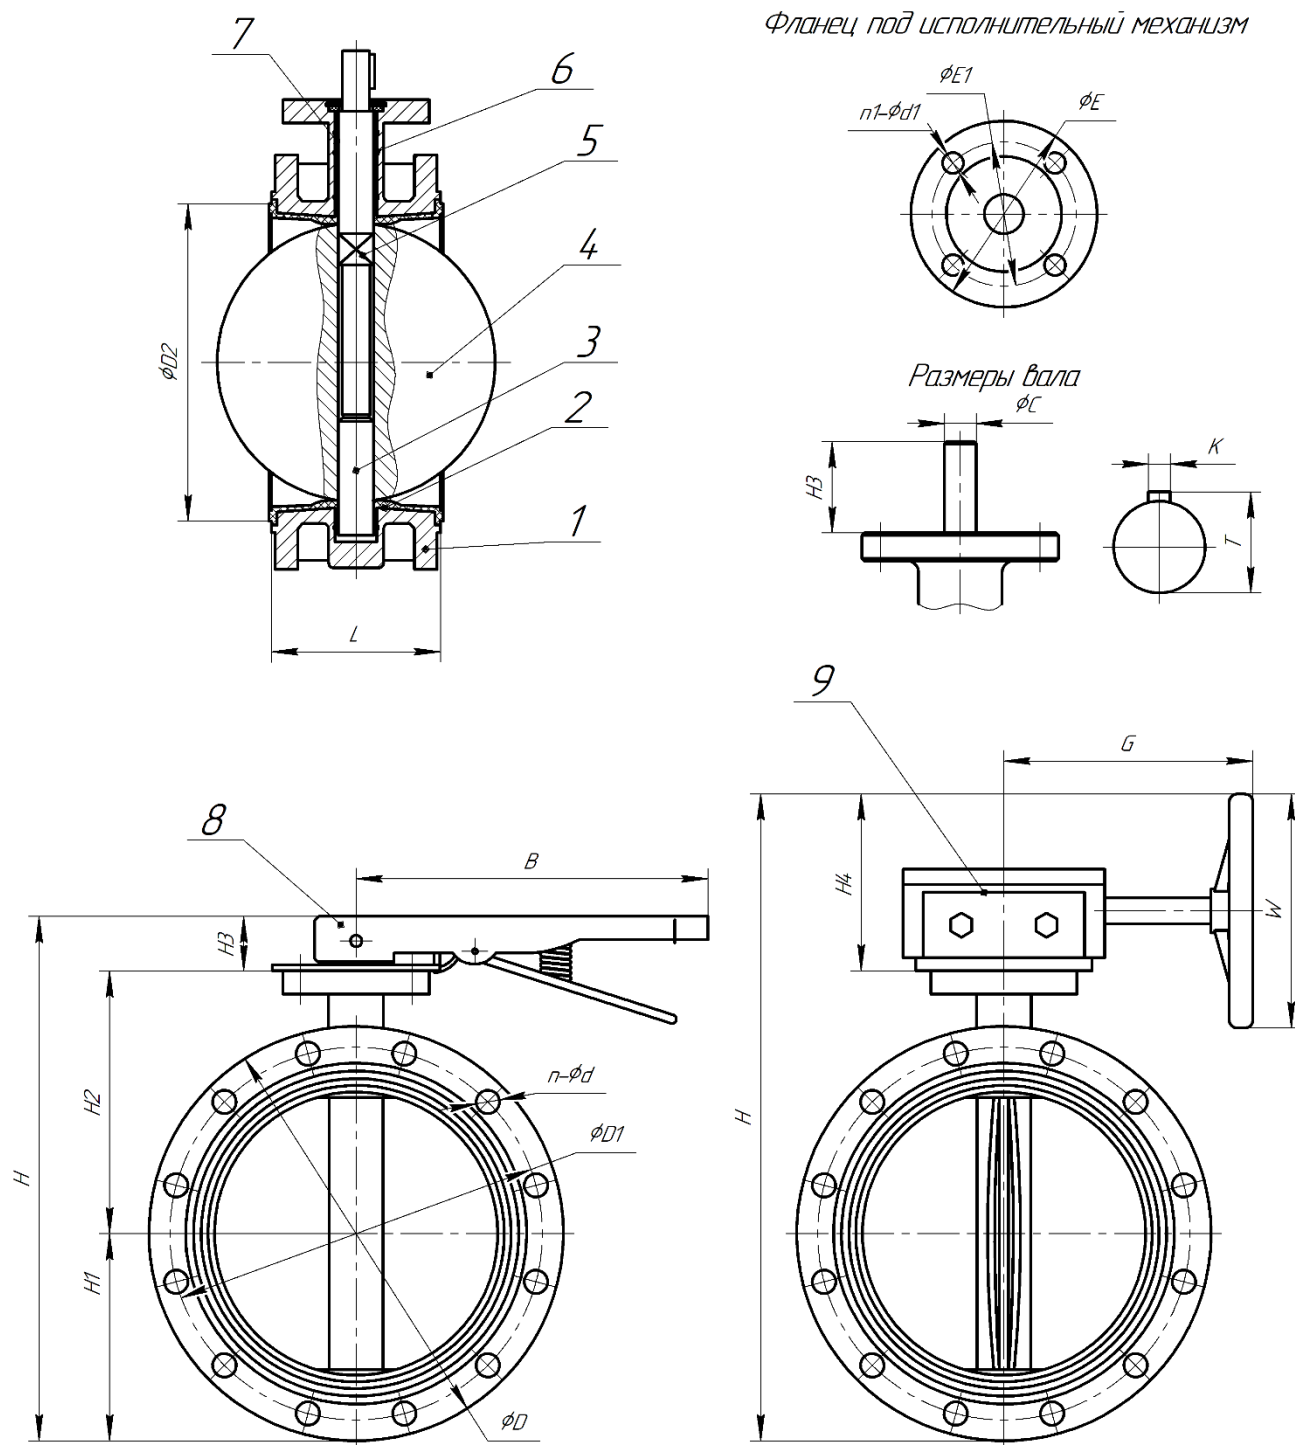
Затвор с рукояткой DN50-300 и редуктором DN50-300
